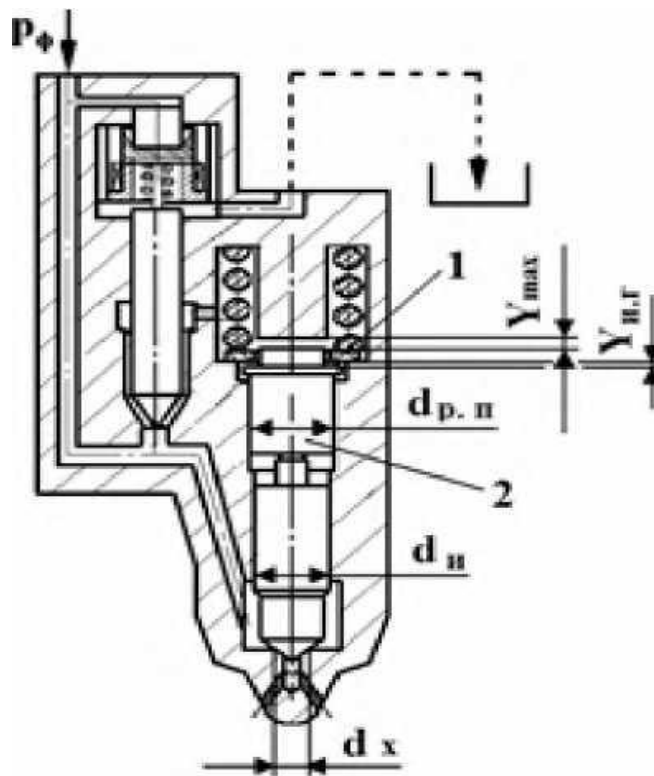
Схема електрогідравлічної форсунки з малогабаритним розпилювачем і робочим поршнем: 1 – рухомий упор; 2 – робочий поршень.
